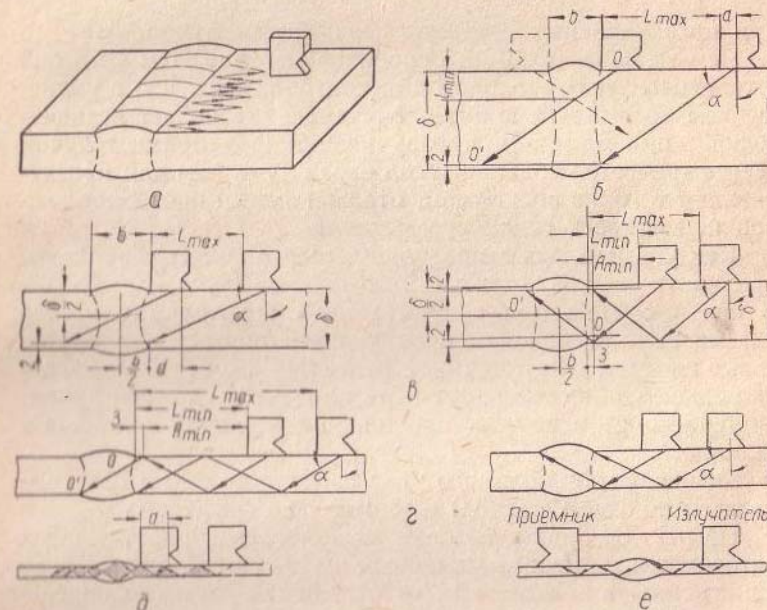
Схемы прозвучивания стыковых сварных швов.
